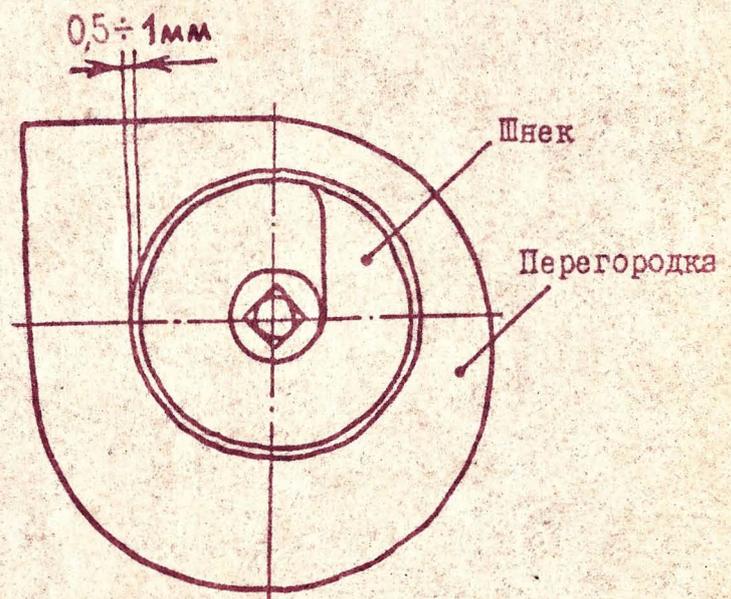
Перегородка между заходной и рабочей частями корпуса для предварительного измельчения продукта
